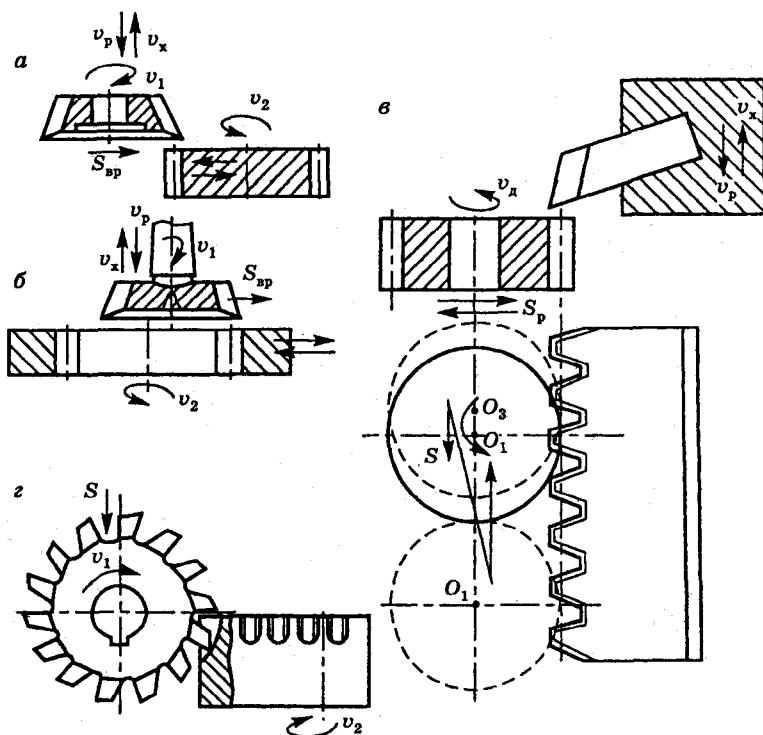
Нарезание цилиндрических зубчатых колес: а, б — зуборезным долбяком; в — зуборезной гребенкой; г — червячной модульной фрезой
